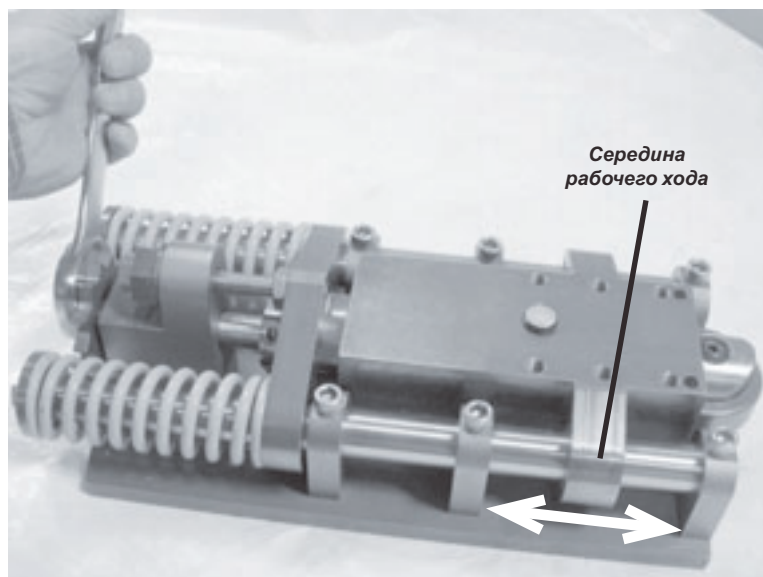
Поверните гайку звездочки по часовой стрелке до расположения суппорта приблизительно в центральной части рабочего хода.
